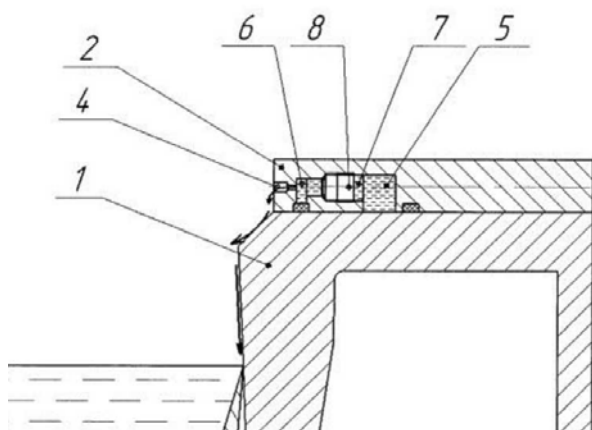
Поперечный разрез кристаллизатора: 1 – корпус кристаллизатора; 2 – крышка кристаллизатора; 4 – выходные отверстия; 5 – проточка со стороны внешнего контура крышки; 6 – проточка со стороны внутреннего контура крышки; 7 – соединительные каналы; 8 – обратные клапаны [90, 104]
